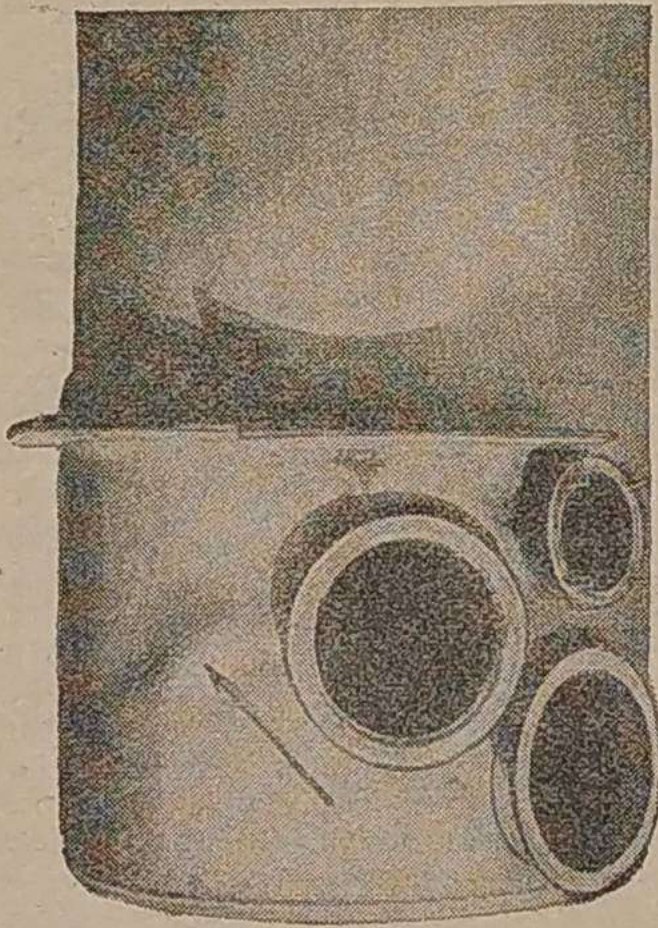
Коробление стенок корпуса газогенератора ЗИС-21.
